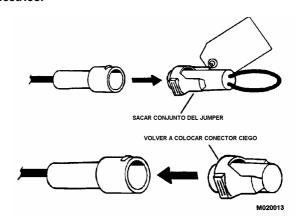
SAQUE EL CONJUNTO DEL JUMPER
